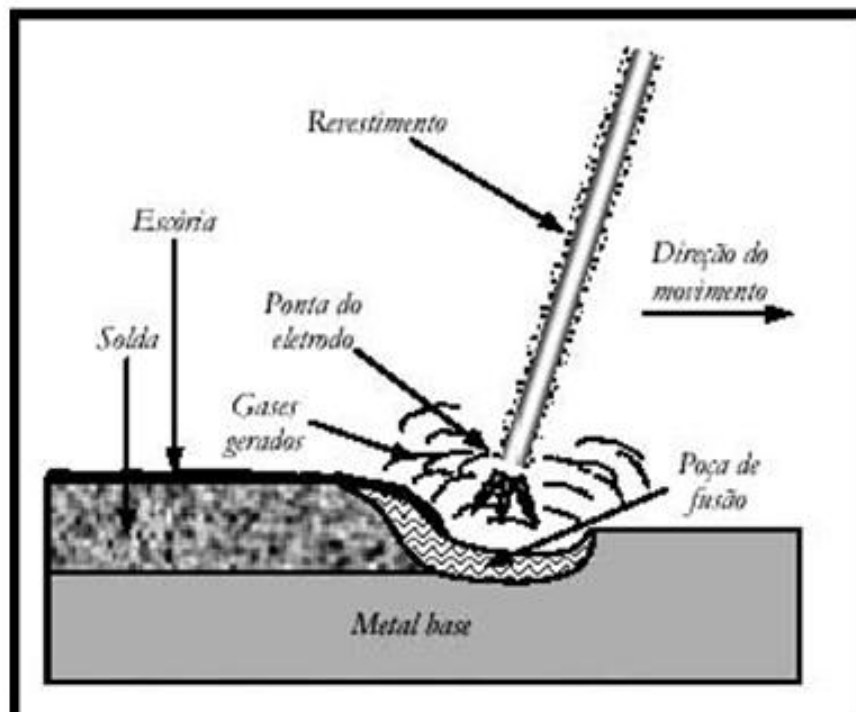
Representação esquemática da soldagem a arco com eletrodo revestido.
